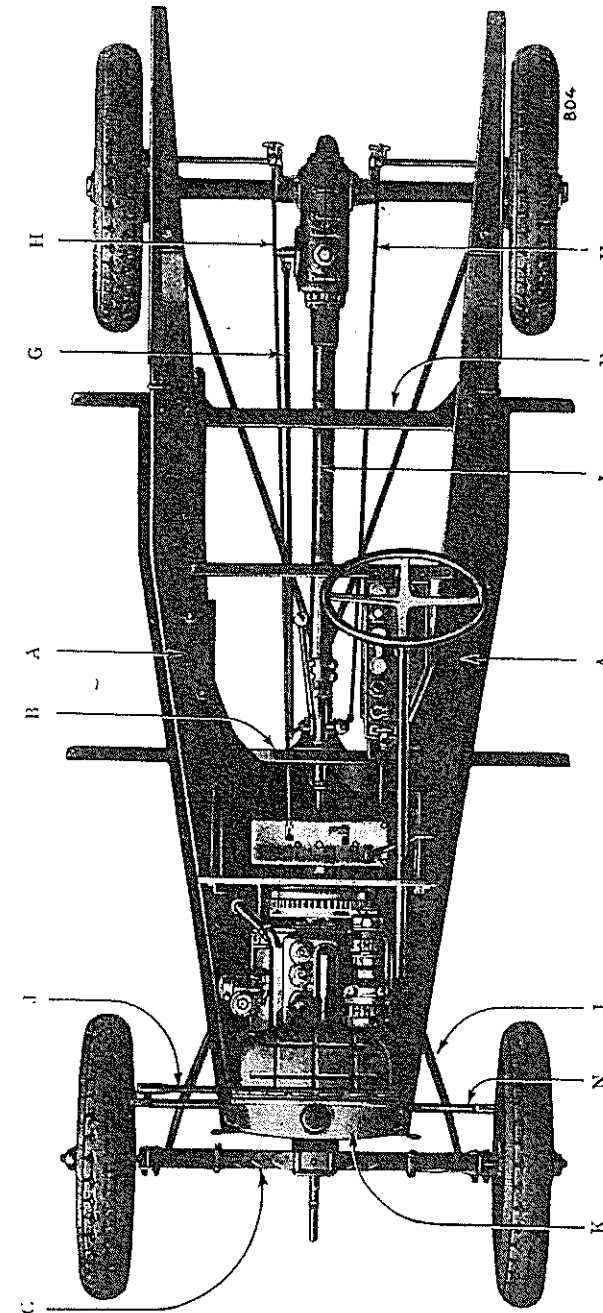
VUE EN PLAN DU CHASSIS 172 R.
